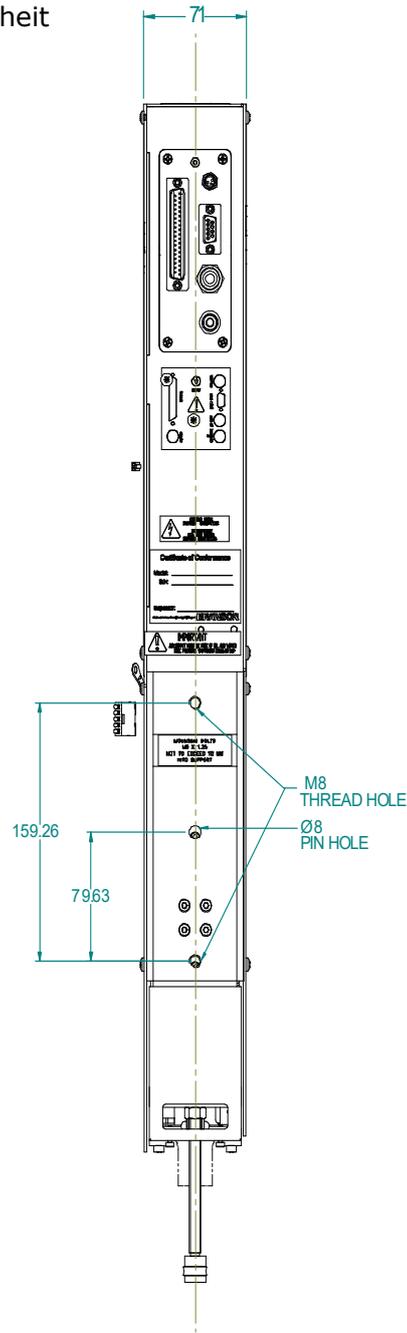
Rückansicht der Vorschubeinheit mit Montagefläche mit den Positionen für Schrauben und Haltestift.
